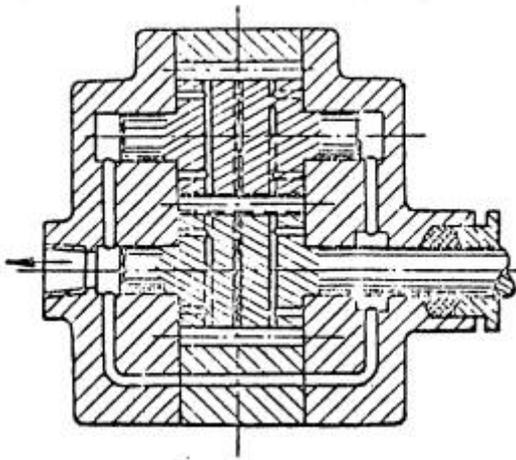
Equilibrado de empujes radiales y axiales en una bomba engranaje
